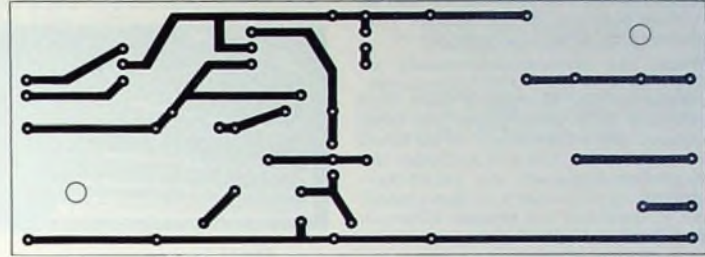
Printplatte II für die Schaltung nach Bild 4 im Maßstab 1:1
